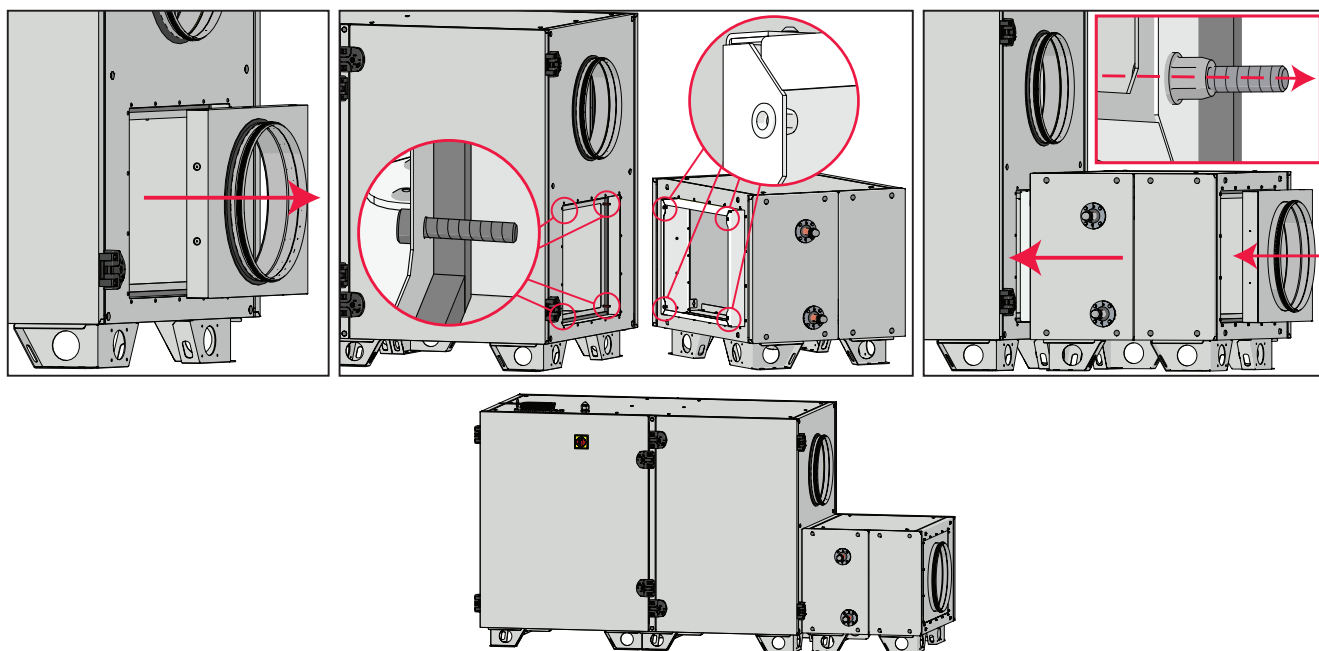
Raccordement d'un dispositif de chauffage/de refroidissement externe
